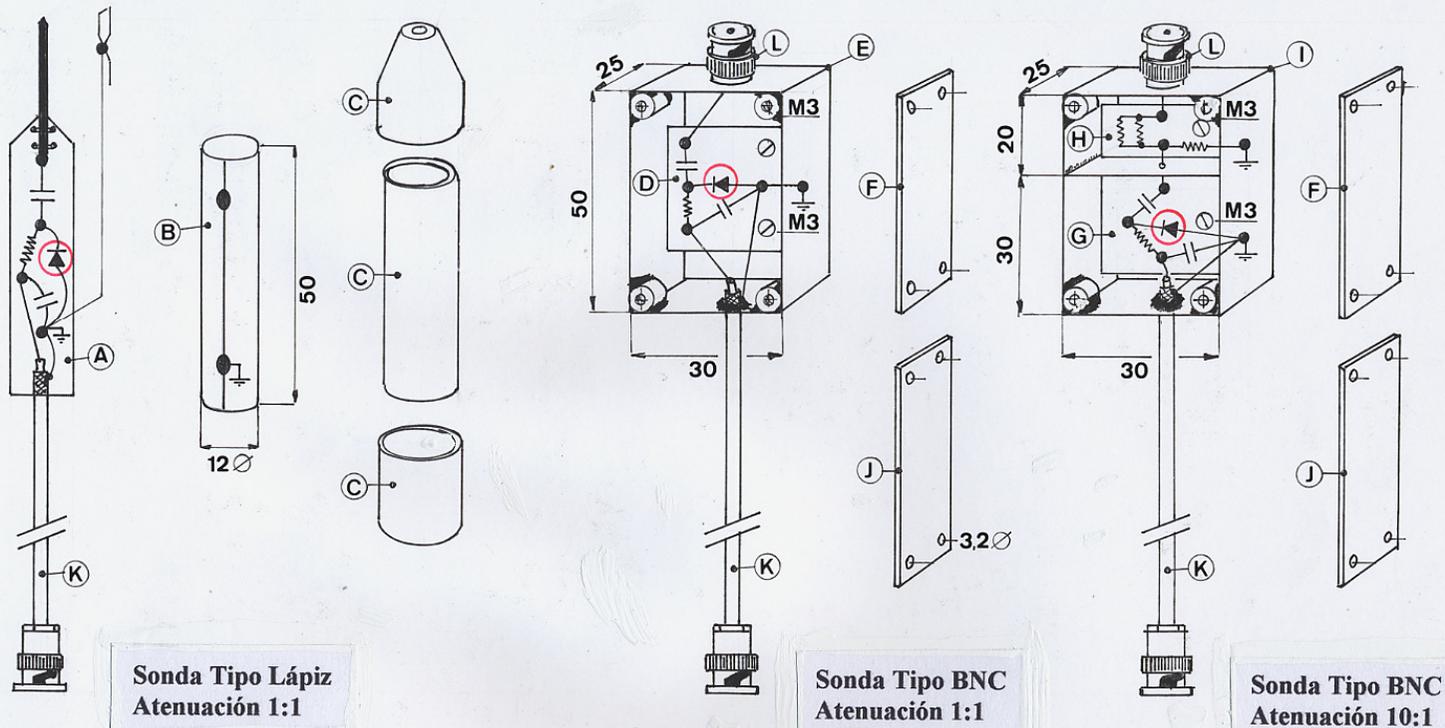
Sondas Demoduladoras de Radio Frecuencia. Detalles constructivos.
